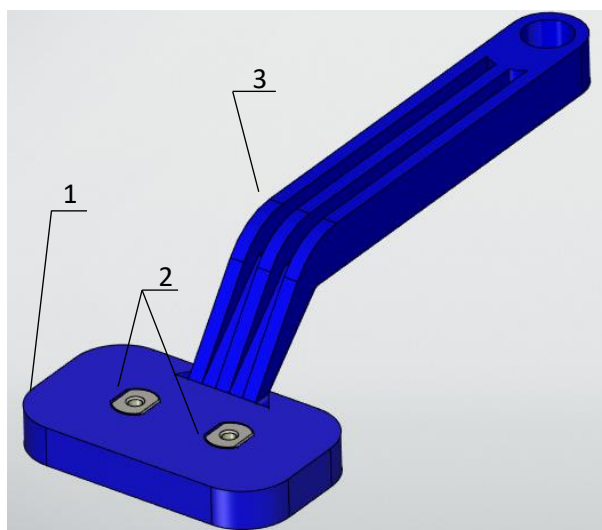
Общий вид пластикового корпуса кондуктора со стальными втулками
